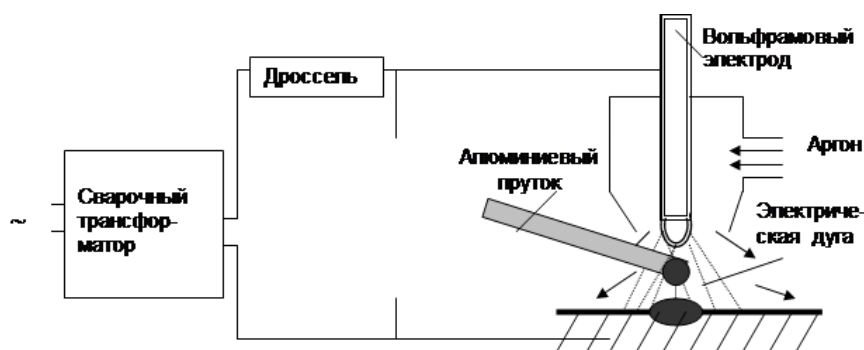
Схема аргоно-дуговой сварки алюминиевых деталей
